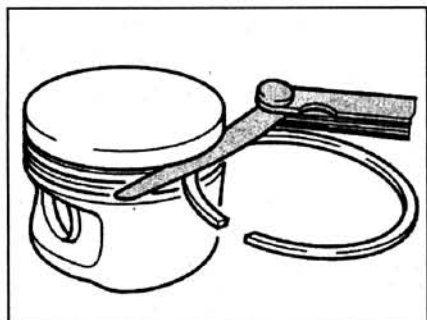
б. Проверка зазора поршневого кольца по высоте.
